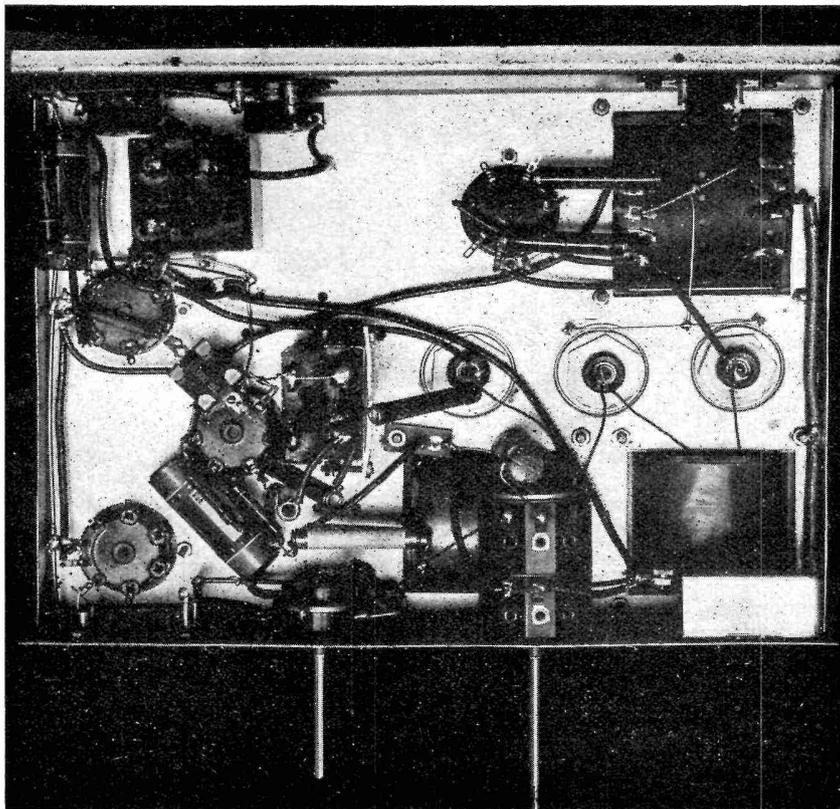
Photographie du châssis de l'ampli vu de dessous.
